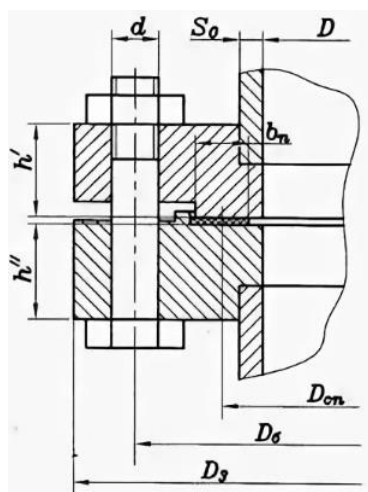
Фланцы с уплотнительной поверхностью типа "выступ-впадина"
